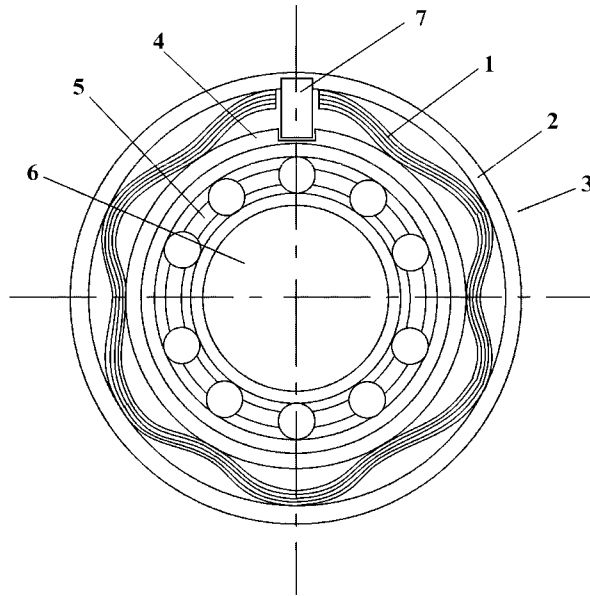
Внешний вид демпфера с саморазгрузкой от веса ротора
